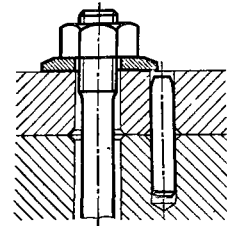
Способ страховки штифта подкладной шайбой под гайку
